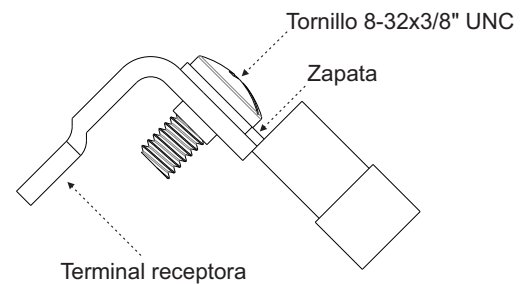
Vista Lateral Izquierda Tornillo 8-32 uniendo una zapata a la terminal receptora del gabinete.
